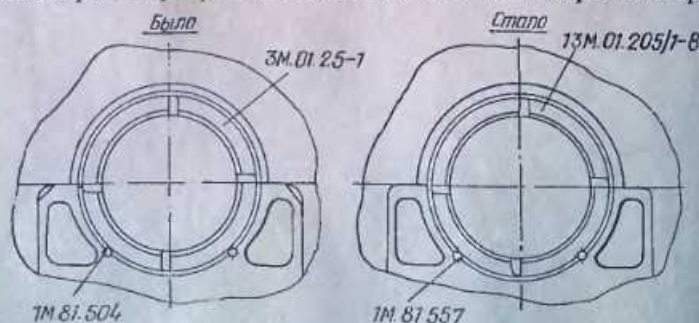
Новое регулировочное кольцо под центральную шестерню 1-й подвески
